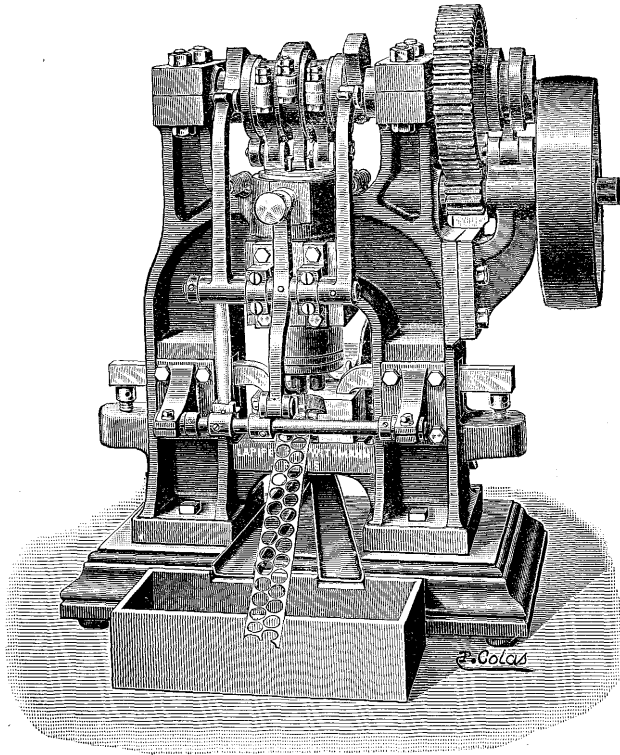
Machine à découper et emboutir, de MM. Lapipe et Wittmann, de Paris.
